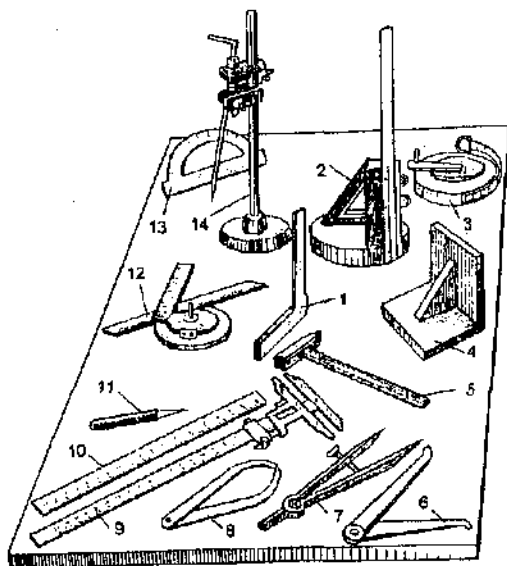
Разметочная плита и инструменты для разметки: 1 — поперечный угольник; 2 — высотомер; 3 — рулетка; 4 — установочный угольник; 5 — молоток; 6 — нутромер; 7 — циркуль; 8 — кроноциркуль; 9 — штангенциркуль с широким упором; 10 — измерительная линейка; 11 — кернер; 12 — угомер; 13 — транспортир; 14 — рейсмус с чертилкой
